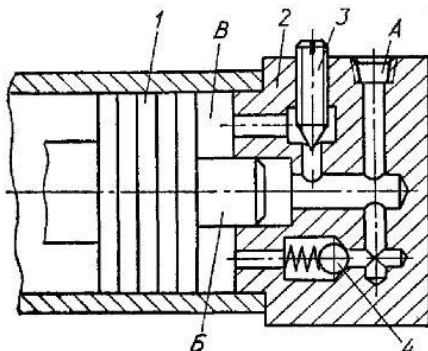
Схема демпфирования штока гидроцилиндра в конце хода
